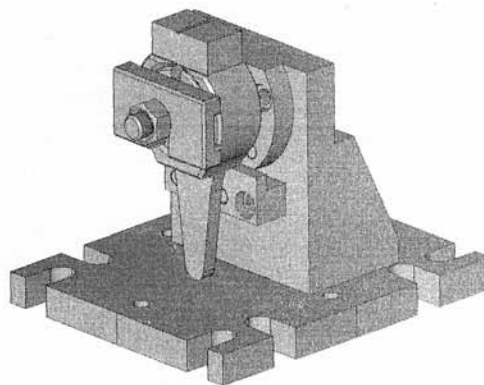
Приспособления с установленной деталью «Головка КЗР1507601»
